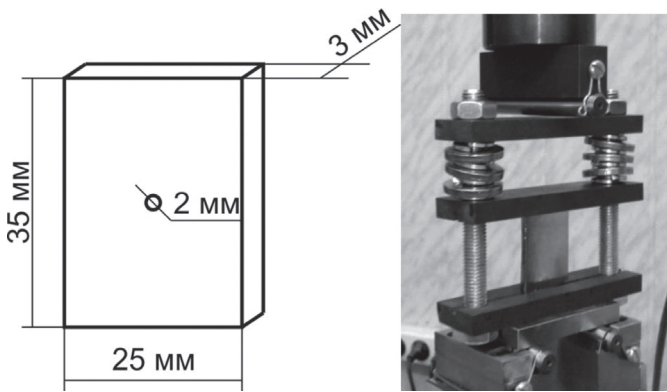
Схема образца и внешний вид приспособления для создания сжимающих напряжений
